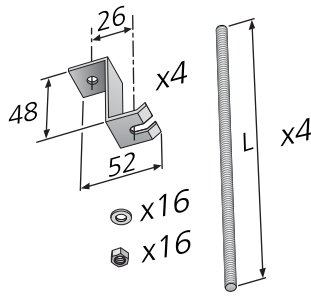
Conjunto de montaje SYST MS-1, fijación para techo y varilla roscada.
